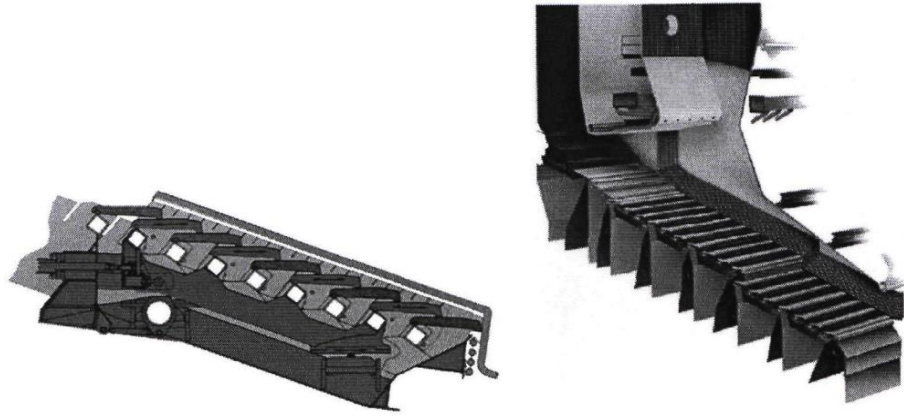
Перештовхуюча колосникова решітка фірми Steinmuller
